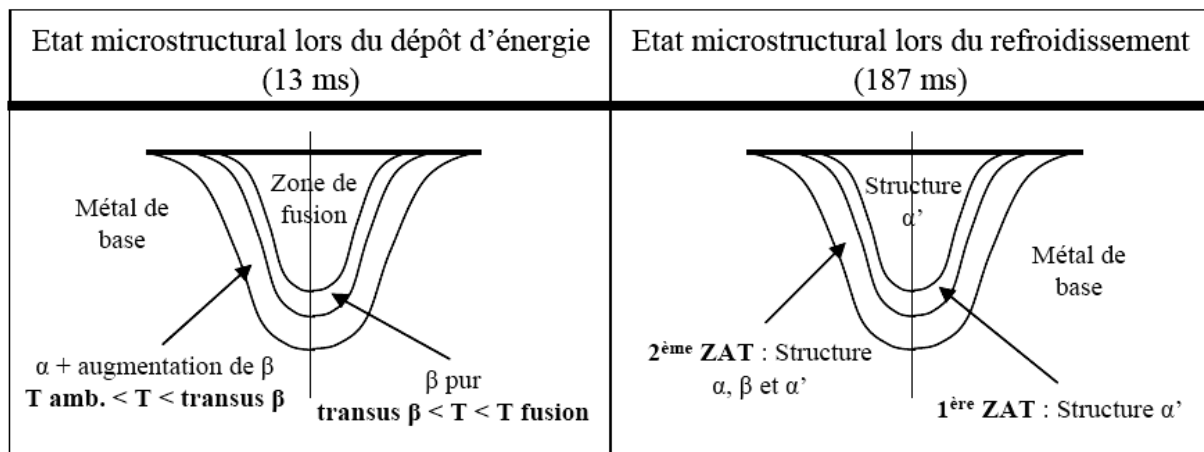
Analyse d'un cordon de soudure pendant le soudage
